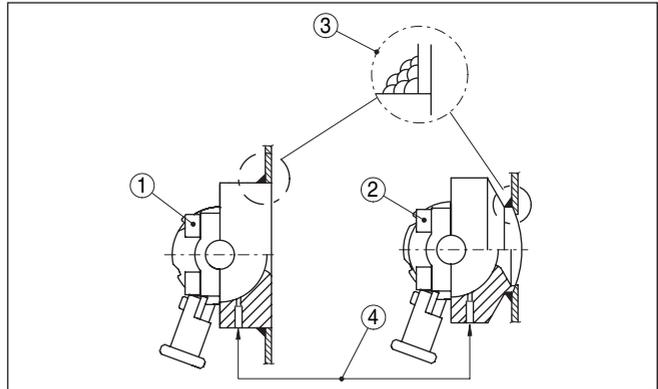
Guarnição de válvula esférica PASVE em modelo soldado
